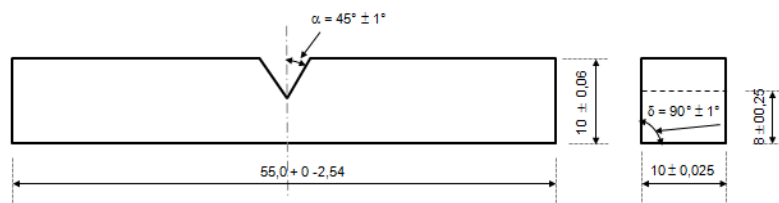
Esboço das dimensões em mm do CP de Charpy conforme ASTM A-370⁽²⁹⁾.
